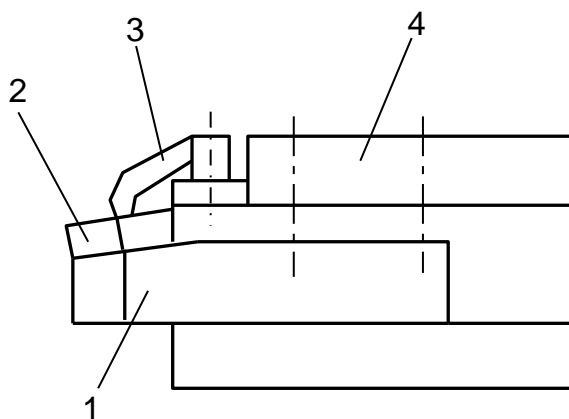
Схема закрепления многогранной режущей пластинки на макете:
